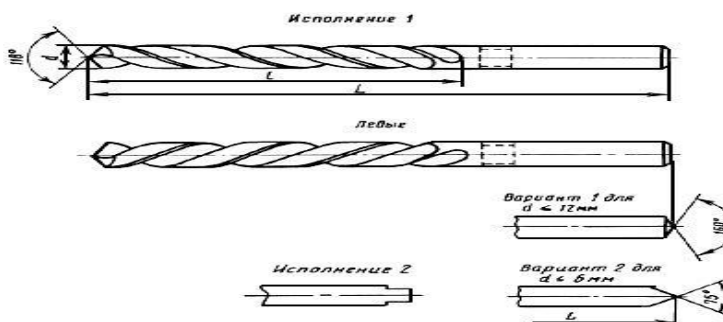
Сверло 2300– 7515 ГОСТ 10902– 77.
